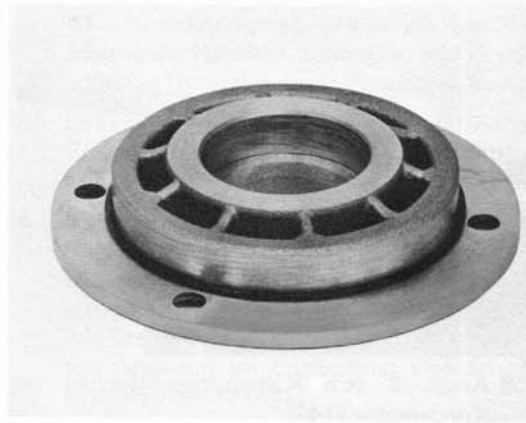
Hinteres Lagergehäuse mit O-Ring
